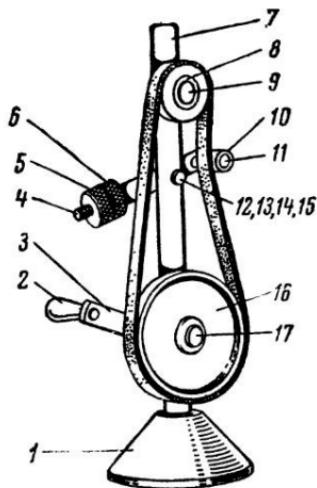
Модель плоскоременной передачи с натяжным роликом: 1 — основание; 2 — ручка; 3 — рычаг ролика; 4 — рычаг натяжного устройства; 5 — гайка (груз); 6 — контргайка (груз); 7 — стойка; 8 — ведомый шкив; 9 — ось ведомого шкива; 10 — натяжной ролик; 11 — ось натяжного ролика; 12 — ось рычага натяжного устройства; 13 — шайба; 14 — гайка; 15 — шплинт; 16 — ведущий шкив; 17 — ведущий вал.
